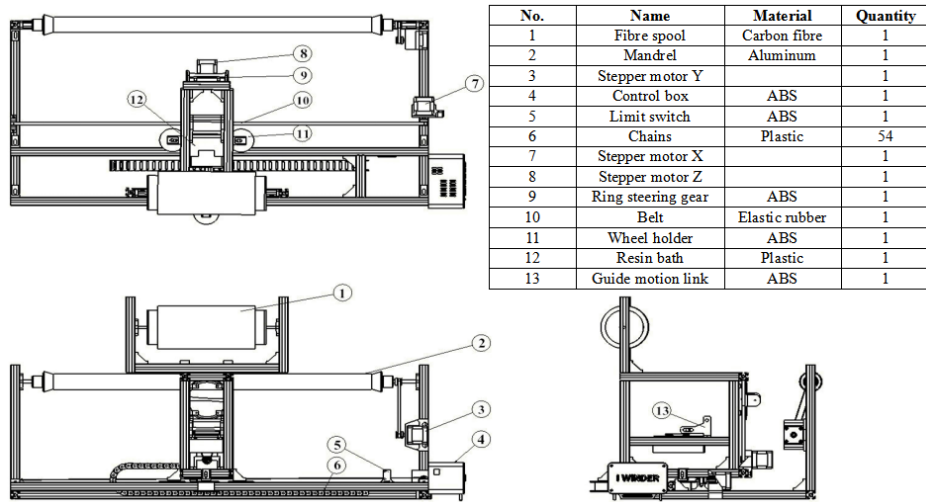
Illustrazione del disegno meccanico di una macchina di FW a 3 g.d.l.. Fonte: [10]
